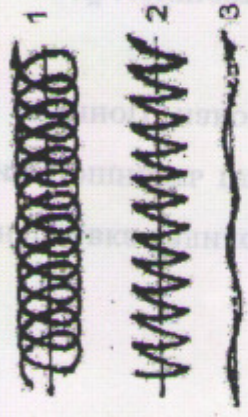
Схемы колебательных движений мундштука: 1 – по спирали; 2 – полумесяцем; 3 – с небольшими поперечными колебаниями
